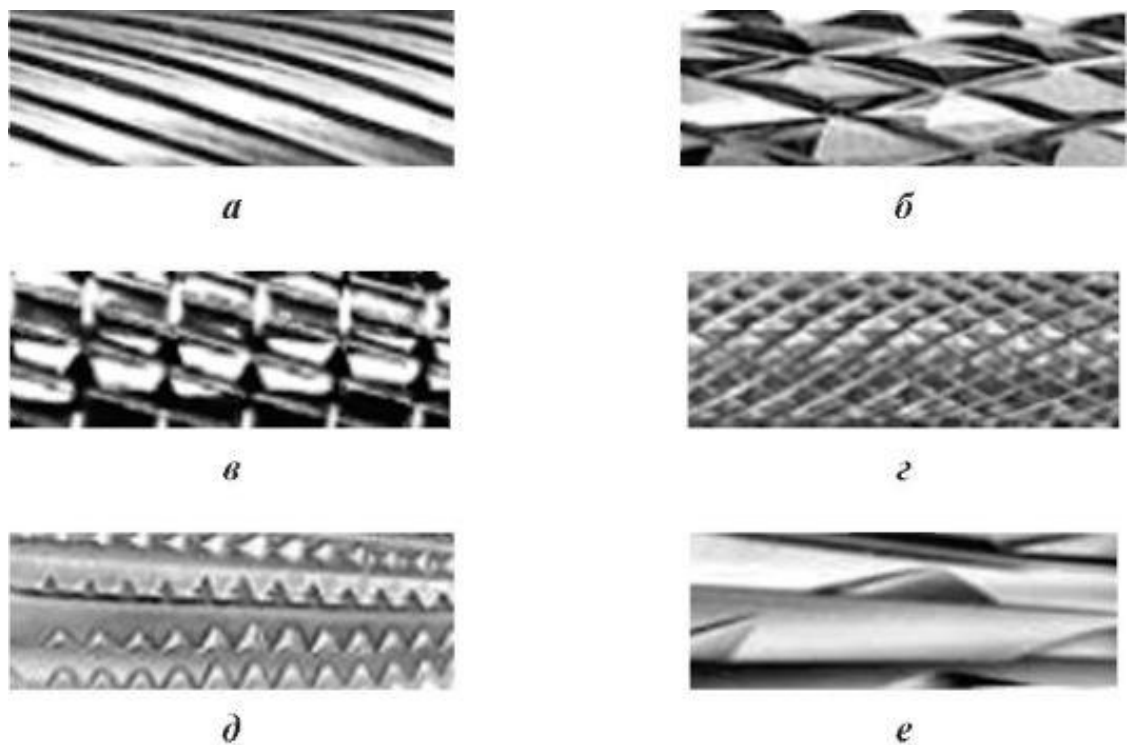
Типи нарізки твердосплавних інструментів: а - однорядна; б - перехресна; в - спіральна; г - призматична; д - поперечна; е - зубчаста.
